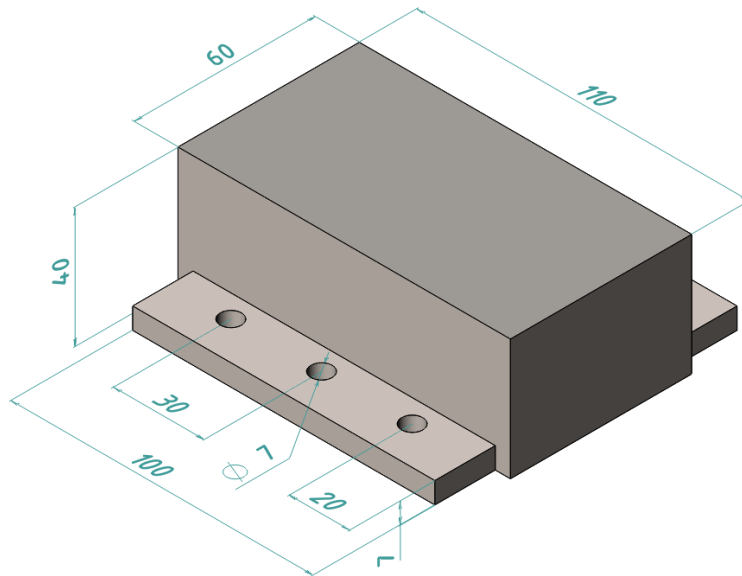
Заготовка загартованої сталі 4X5МФС
